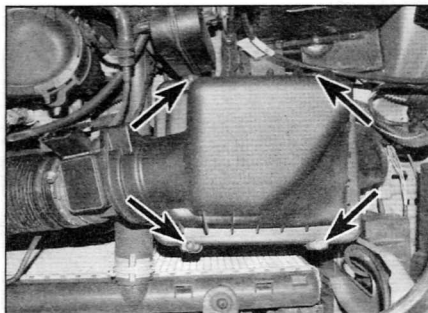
Выверните винты крепления крышки к корпусу воздушного фильтра (поздние двигатели серии DW)
